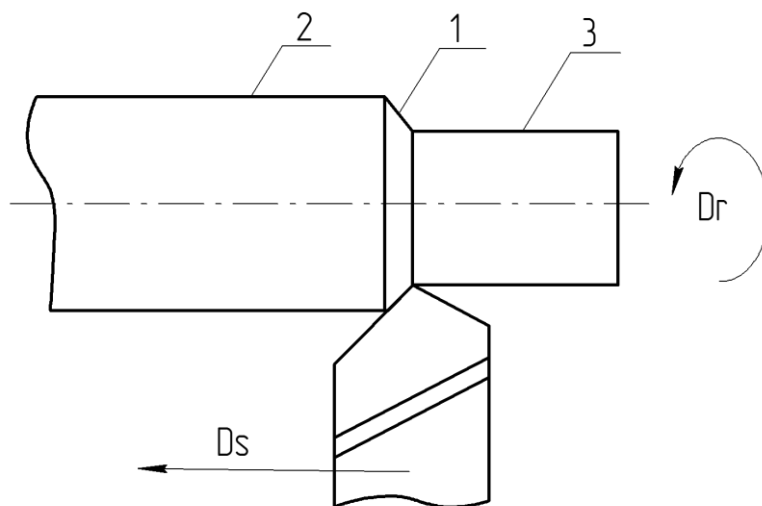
Поверхности на заготовке при токарной обработке
